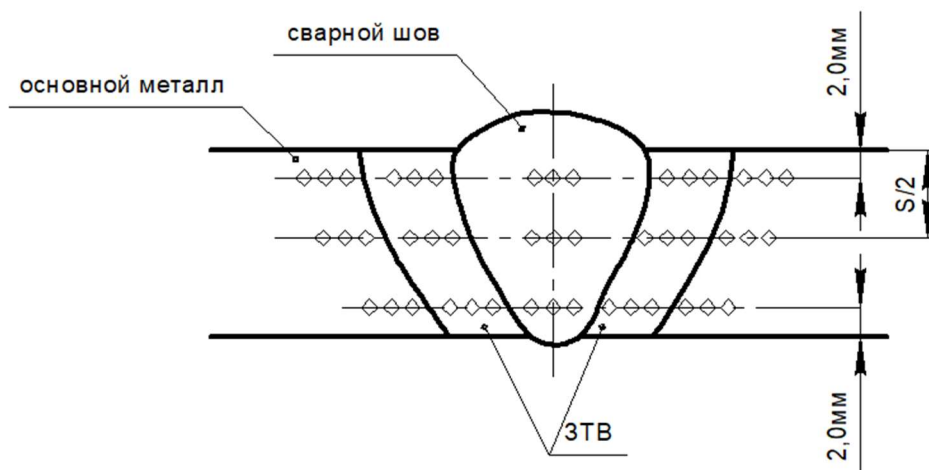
Схема измерения твердости (HV_{10}) в различных зонах стыкового сварного соединения
